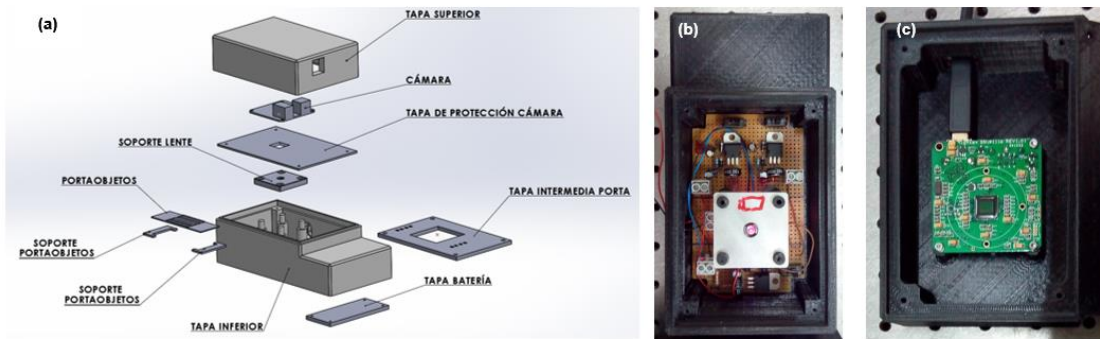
(a) Diseño de los principales componentes, (b) Fotografía de la caja inferior fabricada, (c) Fotografía de la caja superior fabricada.
